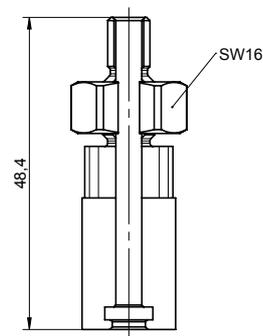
Ausziehvorrichtung, Typ 6419A23B zu Montageadapter
